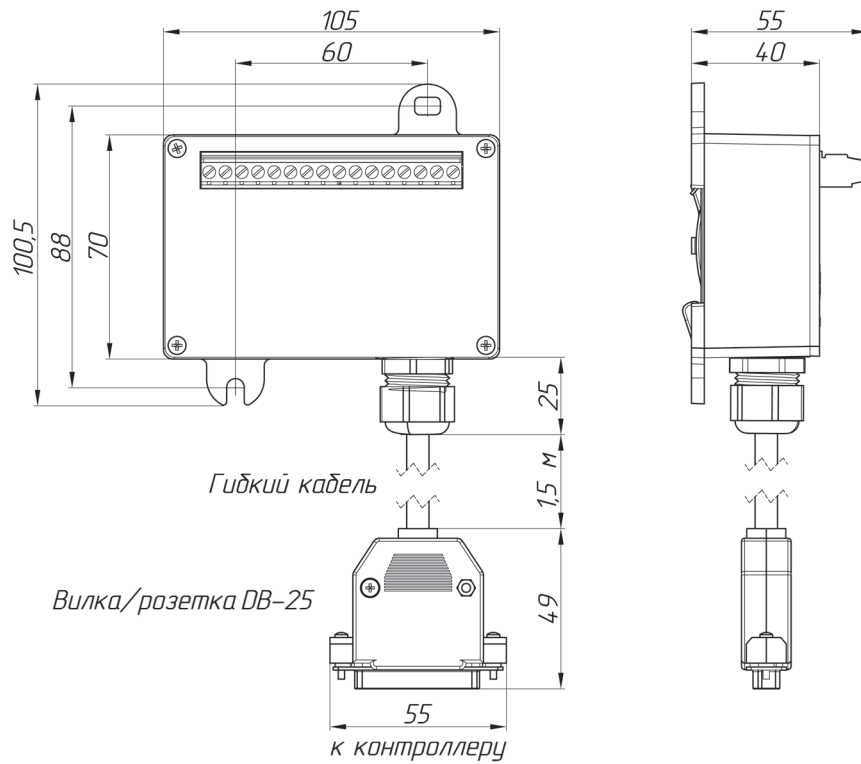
Внешний вид коробки клеммной: код вида 03, 05
